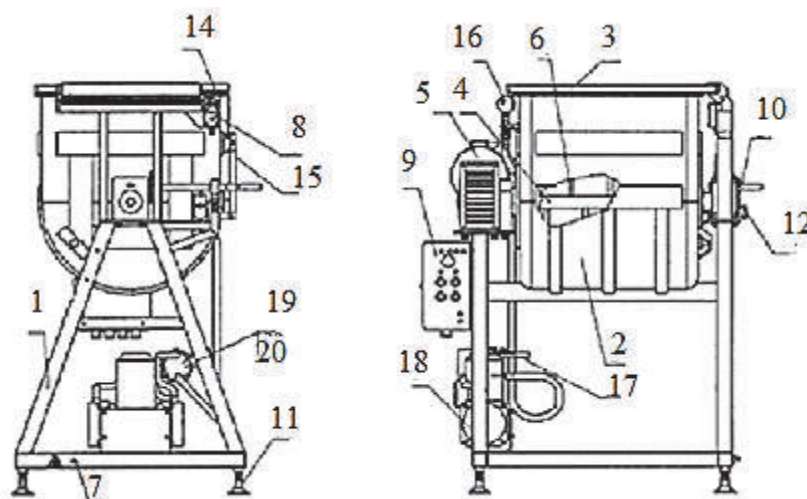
Фаршемешалка лопастная: 1 – каркас, 2 – дежа, 3 – крышка, 4 – мешалка, 5 – мотор-редуктор, 6 – лопасть, 7 – болт заземления, 8 – выключатель путевой, 9 – блок управления, 10 – редуктор червячный, 11 – опора винтовая, 12 – устройство фиксирующее, 13 – пост кнопочный «Выгрузка», 14 – прокладка, 15 – амортизатор, 16 – вакуумметр, 17 – винт, 18 – насос вакуумный, 19 – банка, 20 – шланг
